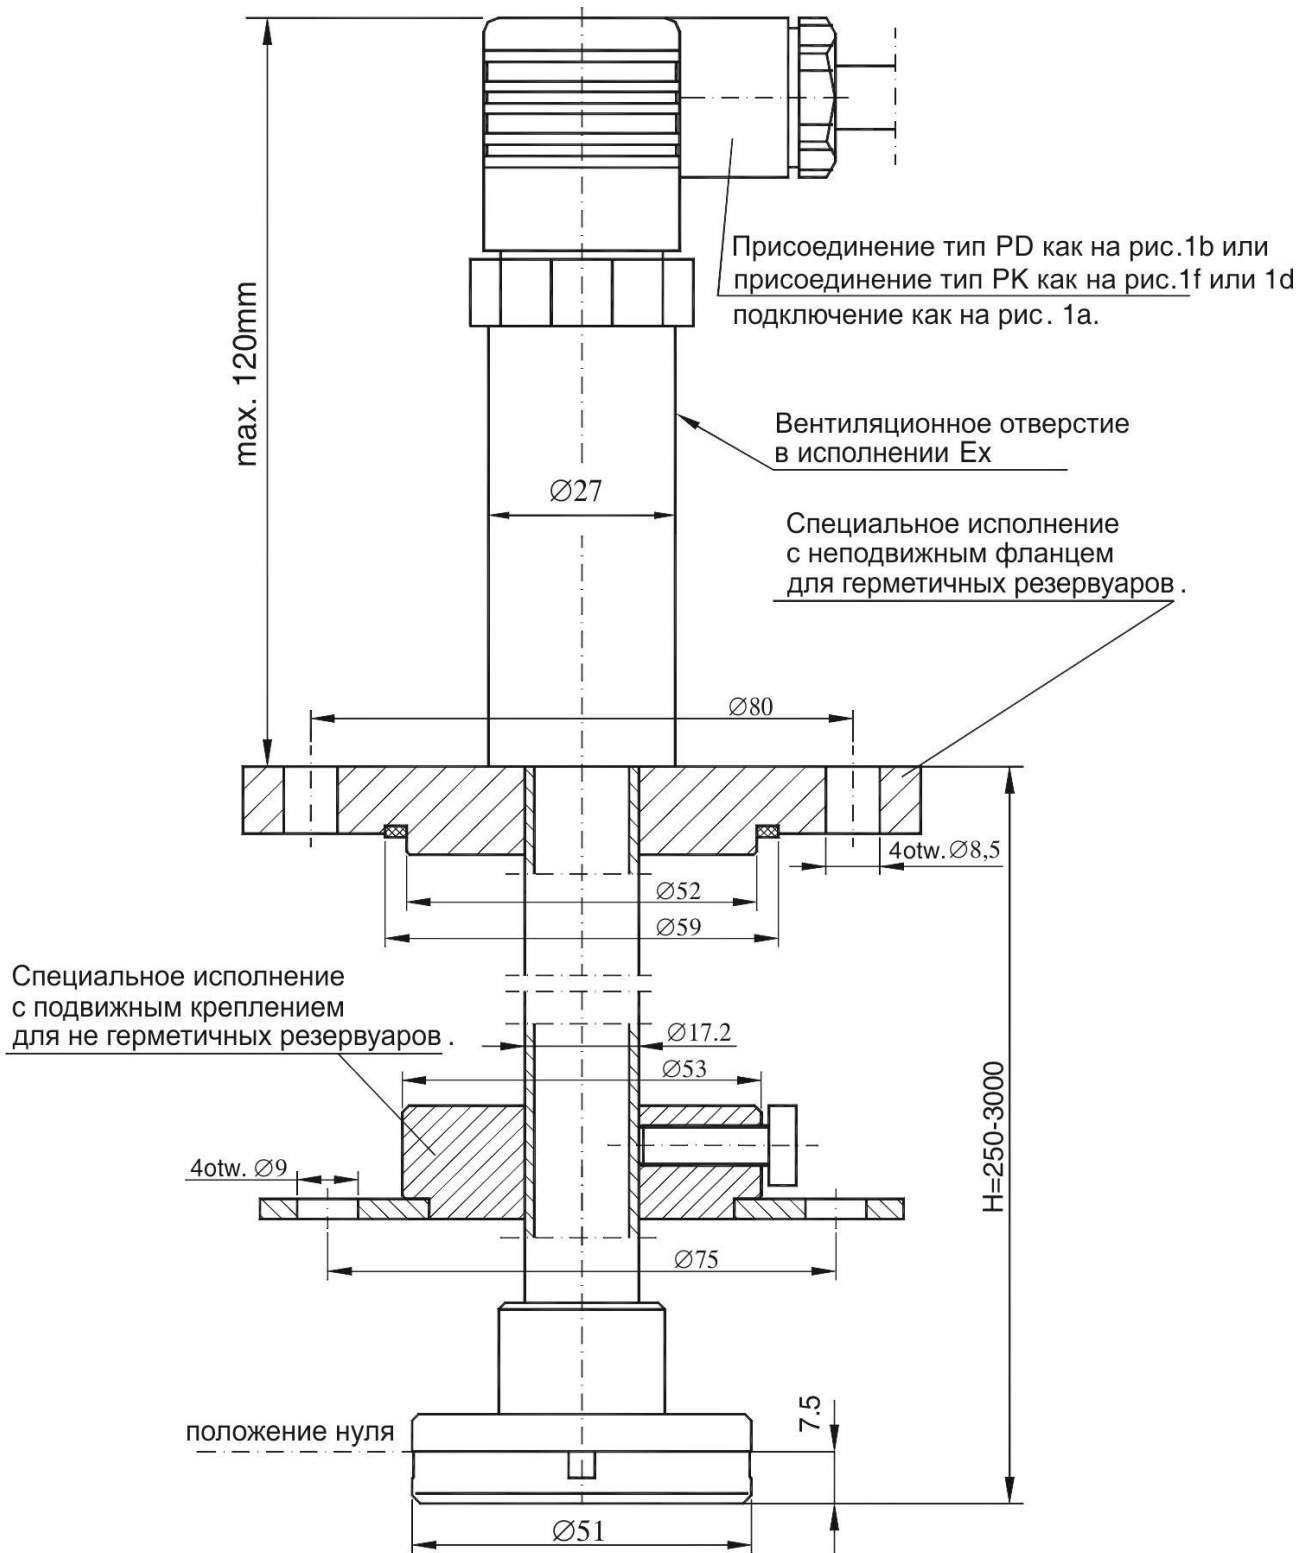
Преобразователь РС-28Р. Габаритные размеры.
